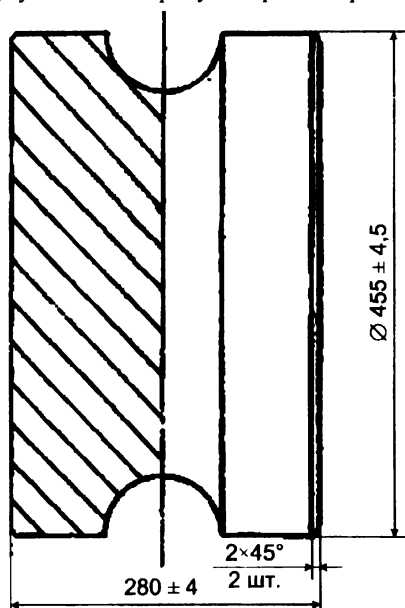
Эскиз валка калибровочного стана ТПЦ 2
